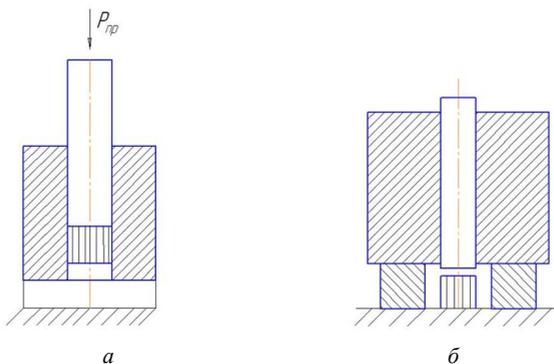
Схемы одностороннего прессования (а) и выпрессовки (б) изделия
